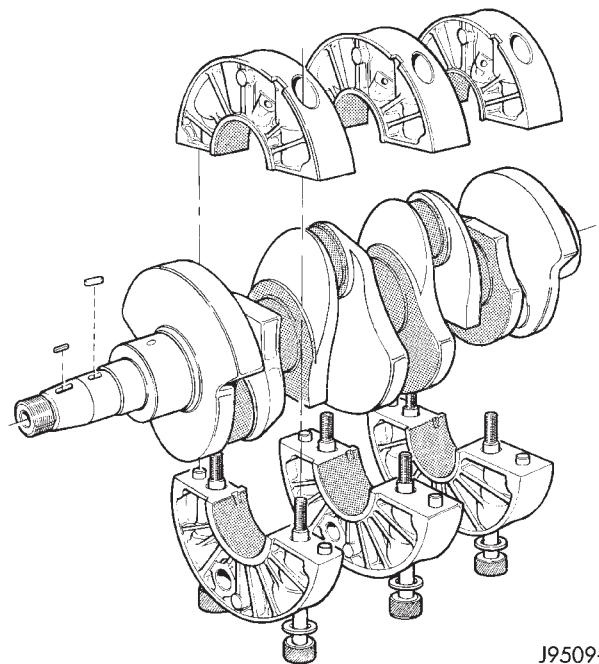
Conjunto de cigüeñal y cojinete de portador
